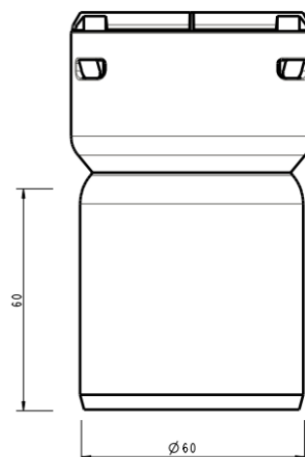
Schéma en coupe d'un conduit Alsace
